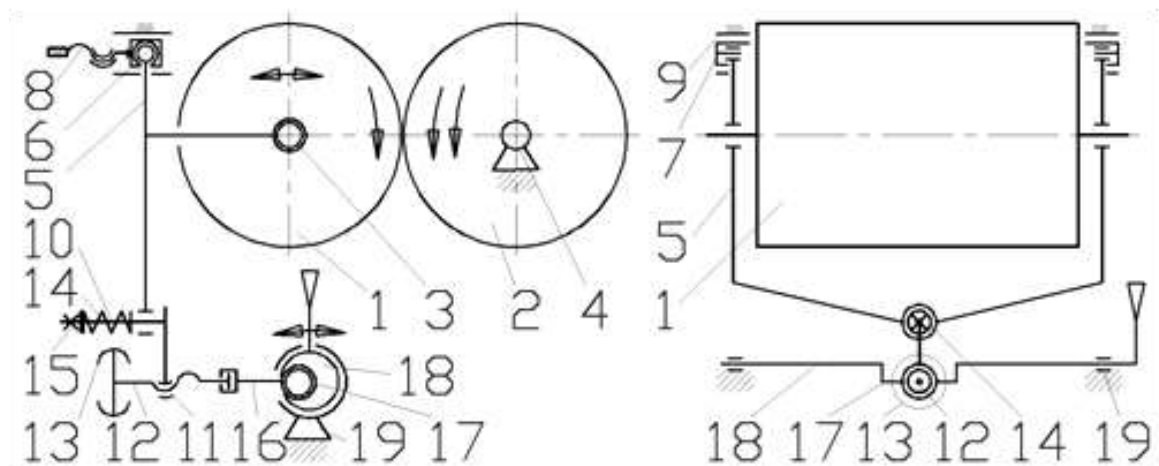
Схема установчого механізму вальцьового верстата.
